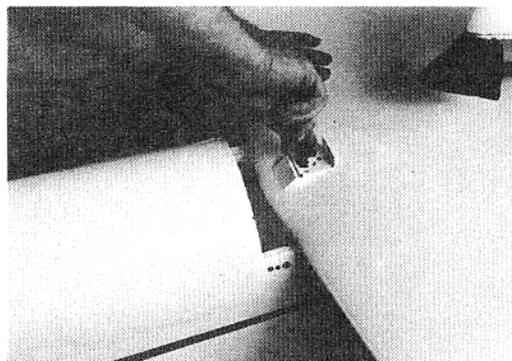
Fixation avant du plan fixe sur axe vertical. Montage et démontage rapides par écrou à oreilles.
